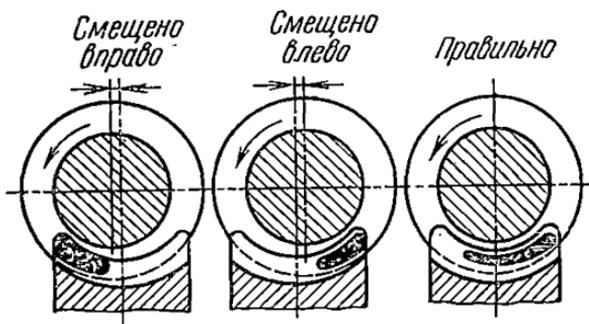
Расположение пятна контакта на зубе червячного колеса.
